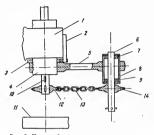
Приспособление к вертикально-сверлильиому станку для расточки ступиц колес сеялок.
